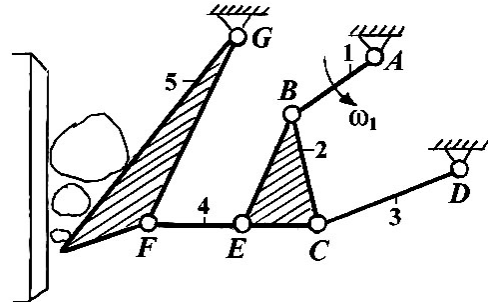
Механизм перемещения подвижной щеки дробилки
